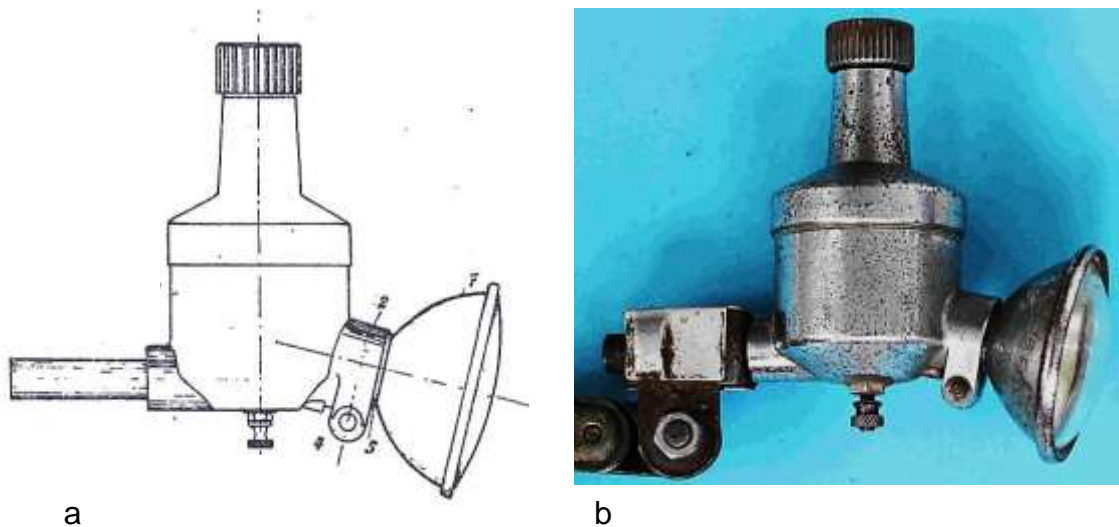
Dynamo mit Lampe: a) Zeichnung im Patent No. 831033, b) Ausgeführte Version (Type 15 P) mit einem Gewicht von 440 g
